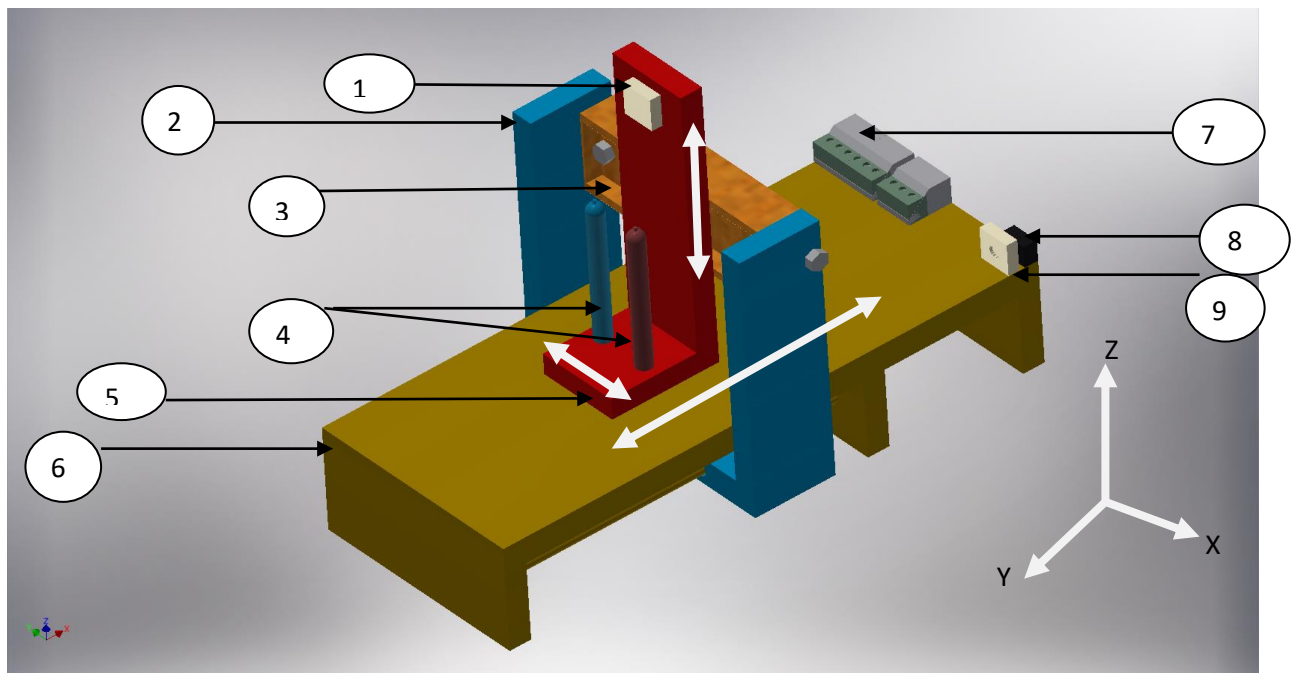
Dessin d'ensemble en 3D de la machine
